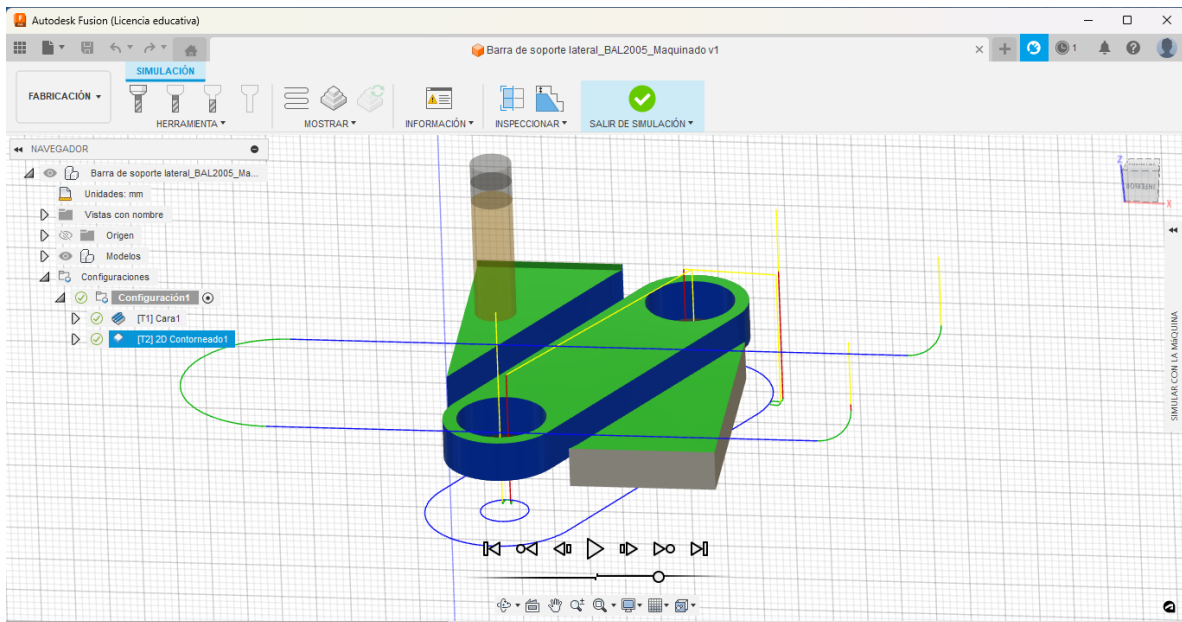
Maquinado de la pieza barra de soporte lateral BAL2005
